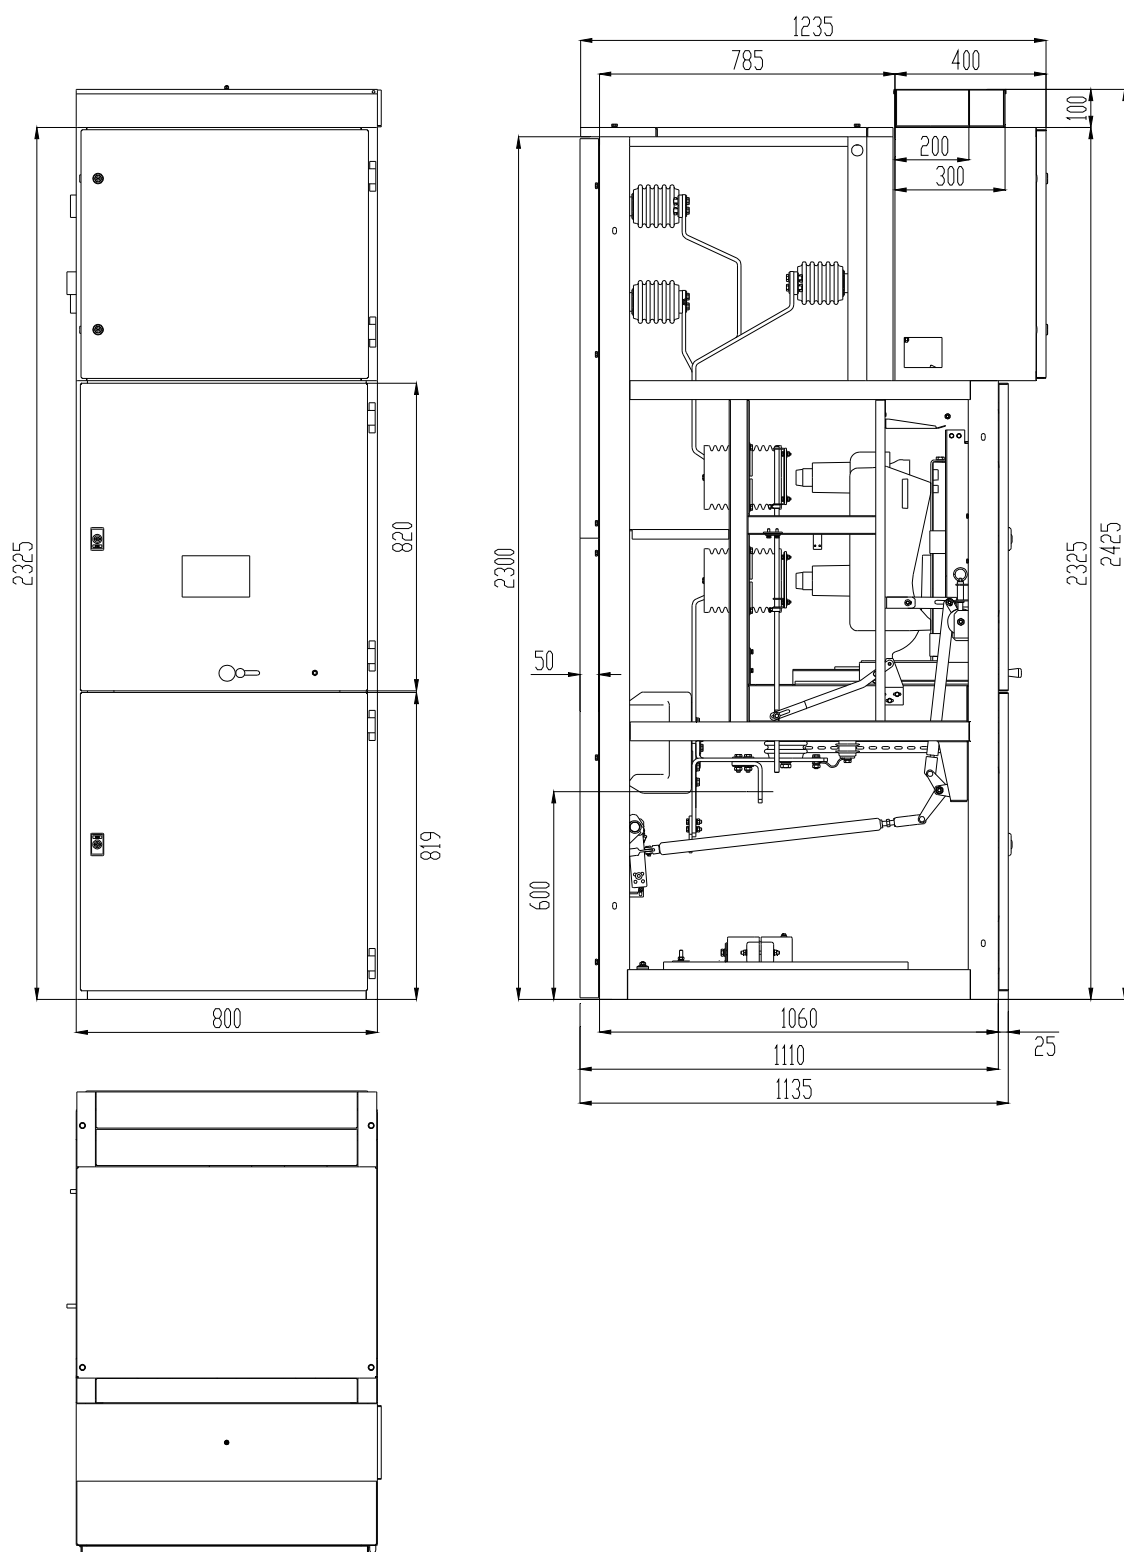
Габаритные размеры шкафов КРУ-БЭМН на номинальный ток 630А – 1250А
